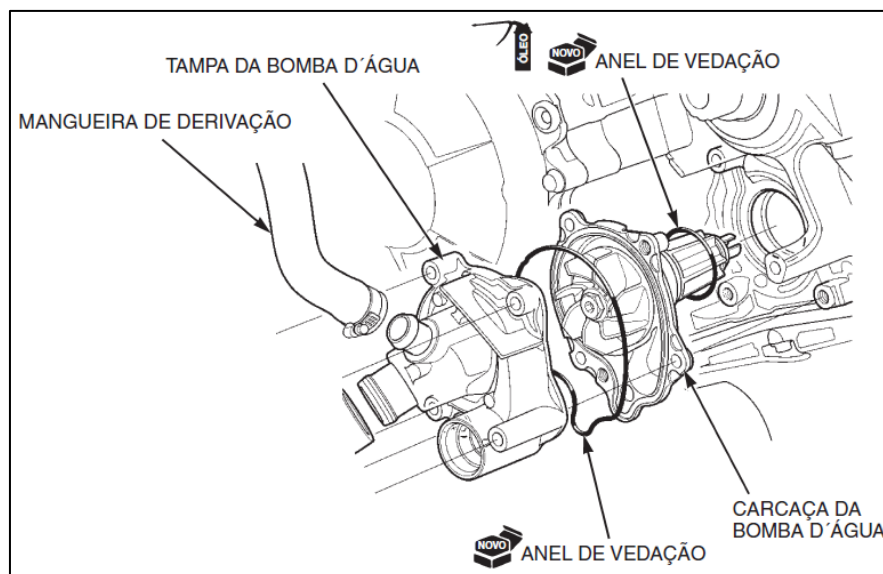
Vista explodida da bomba d'água de um motor Honda CB600 (Honda, 2008).
